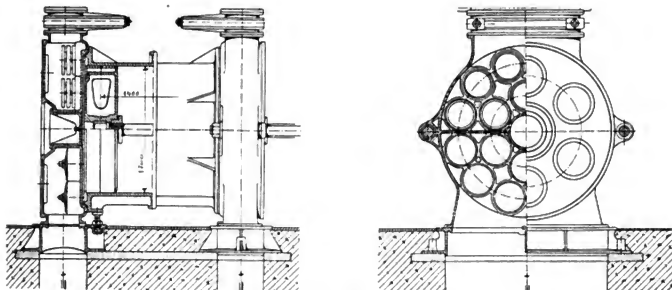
Stumpf-Riedlersches Ventil für schnelllaufende Gebläsemaschinen.
